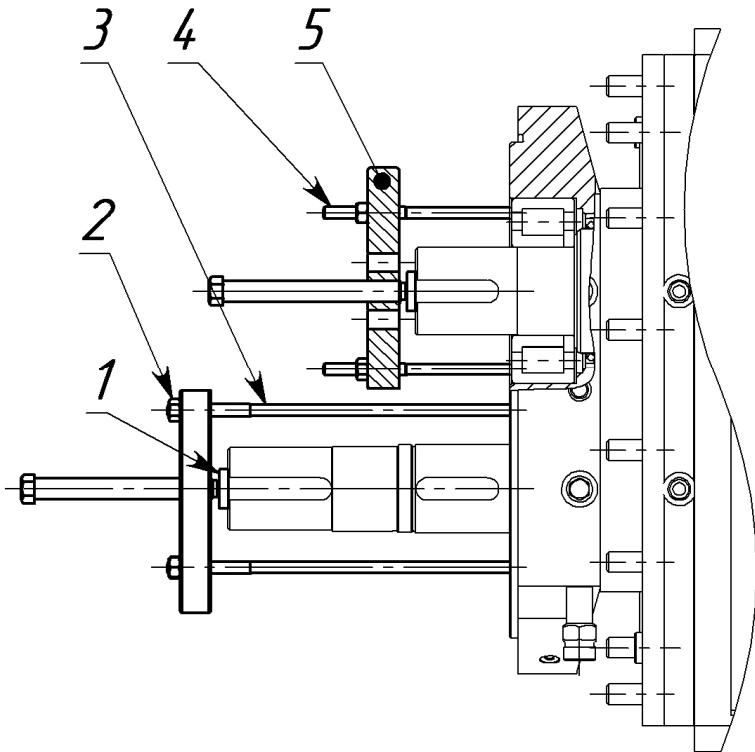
Демонтаж подшипников насоса с приводной стороны
